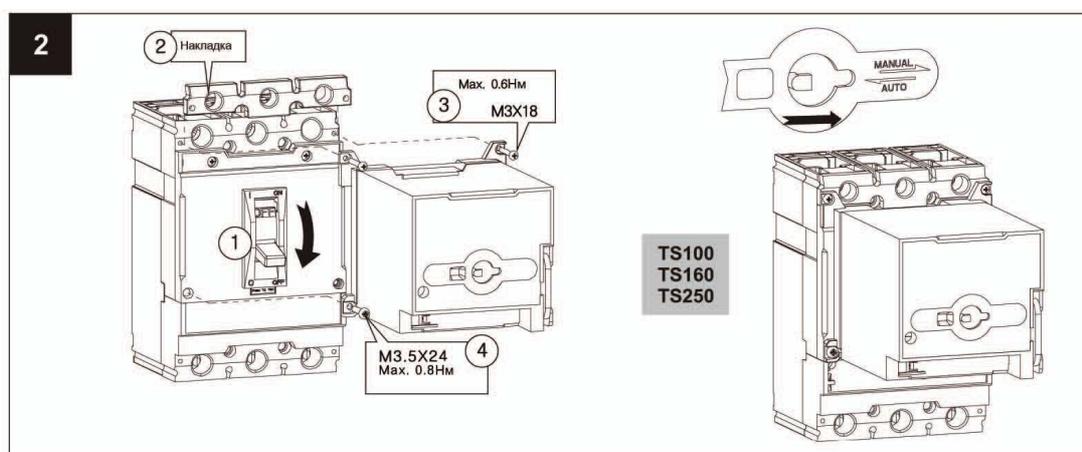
Установка моторного привода на выключатели TS100-TS250
